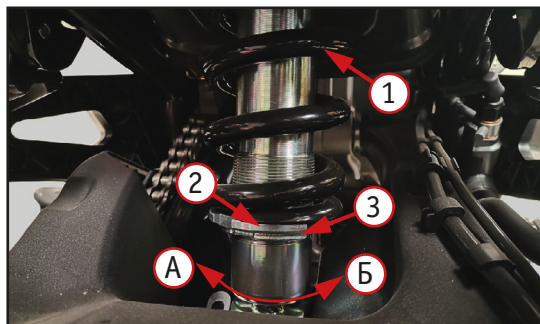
Регулировка преднатяга амортизатора: 1 – пружина; 2 – регулировочная гайка; 3 – стопорная гайка; «А» направление вращения для ослабления преднатяга; «Б» - направление вращения для увеличения преднатяга.
